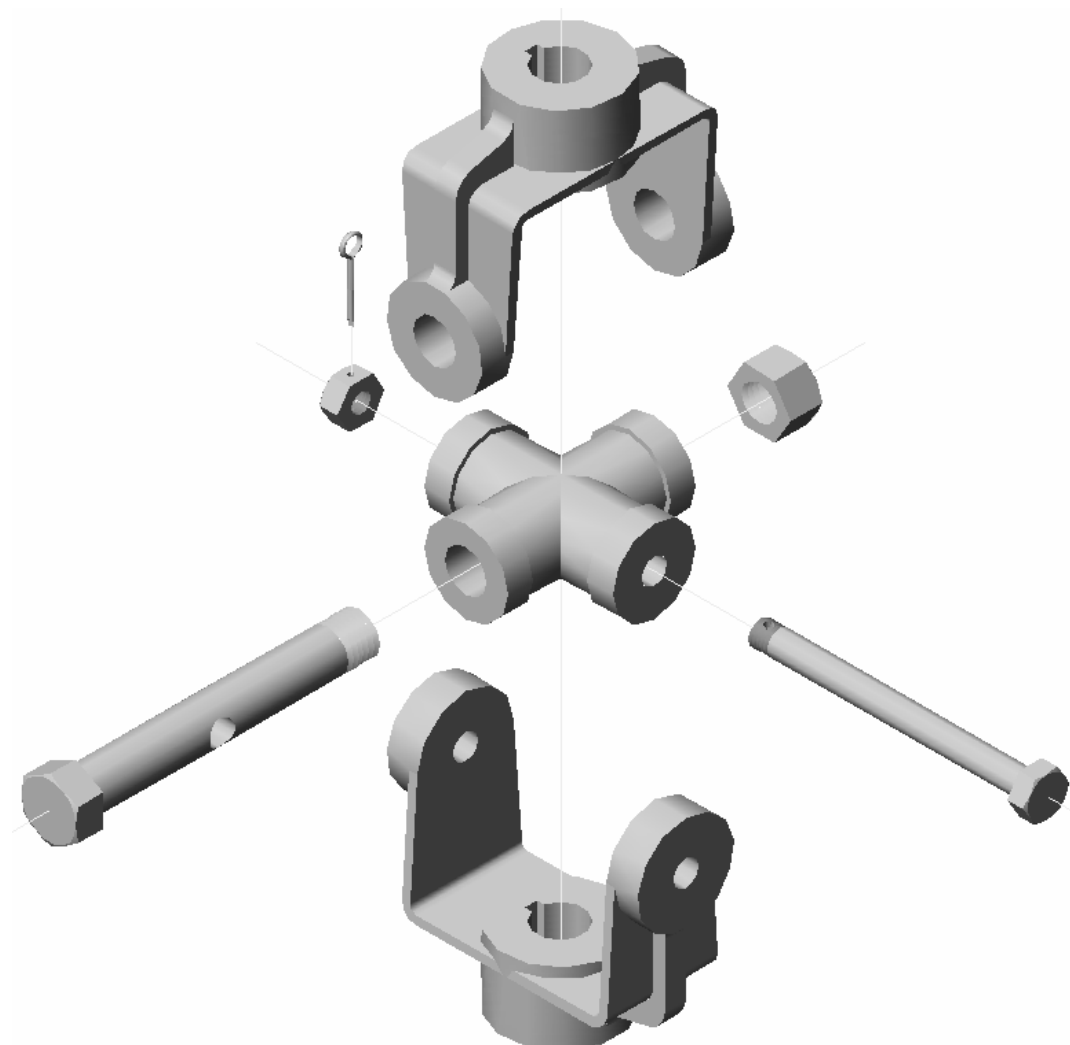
Desenho de conjunto perspético explodido em de uma união *Cardan*.
